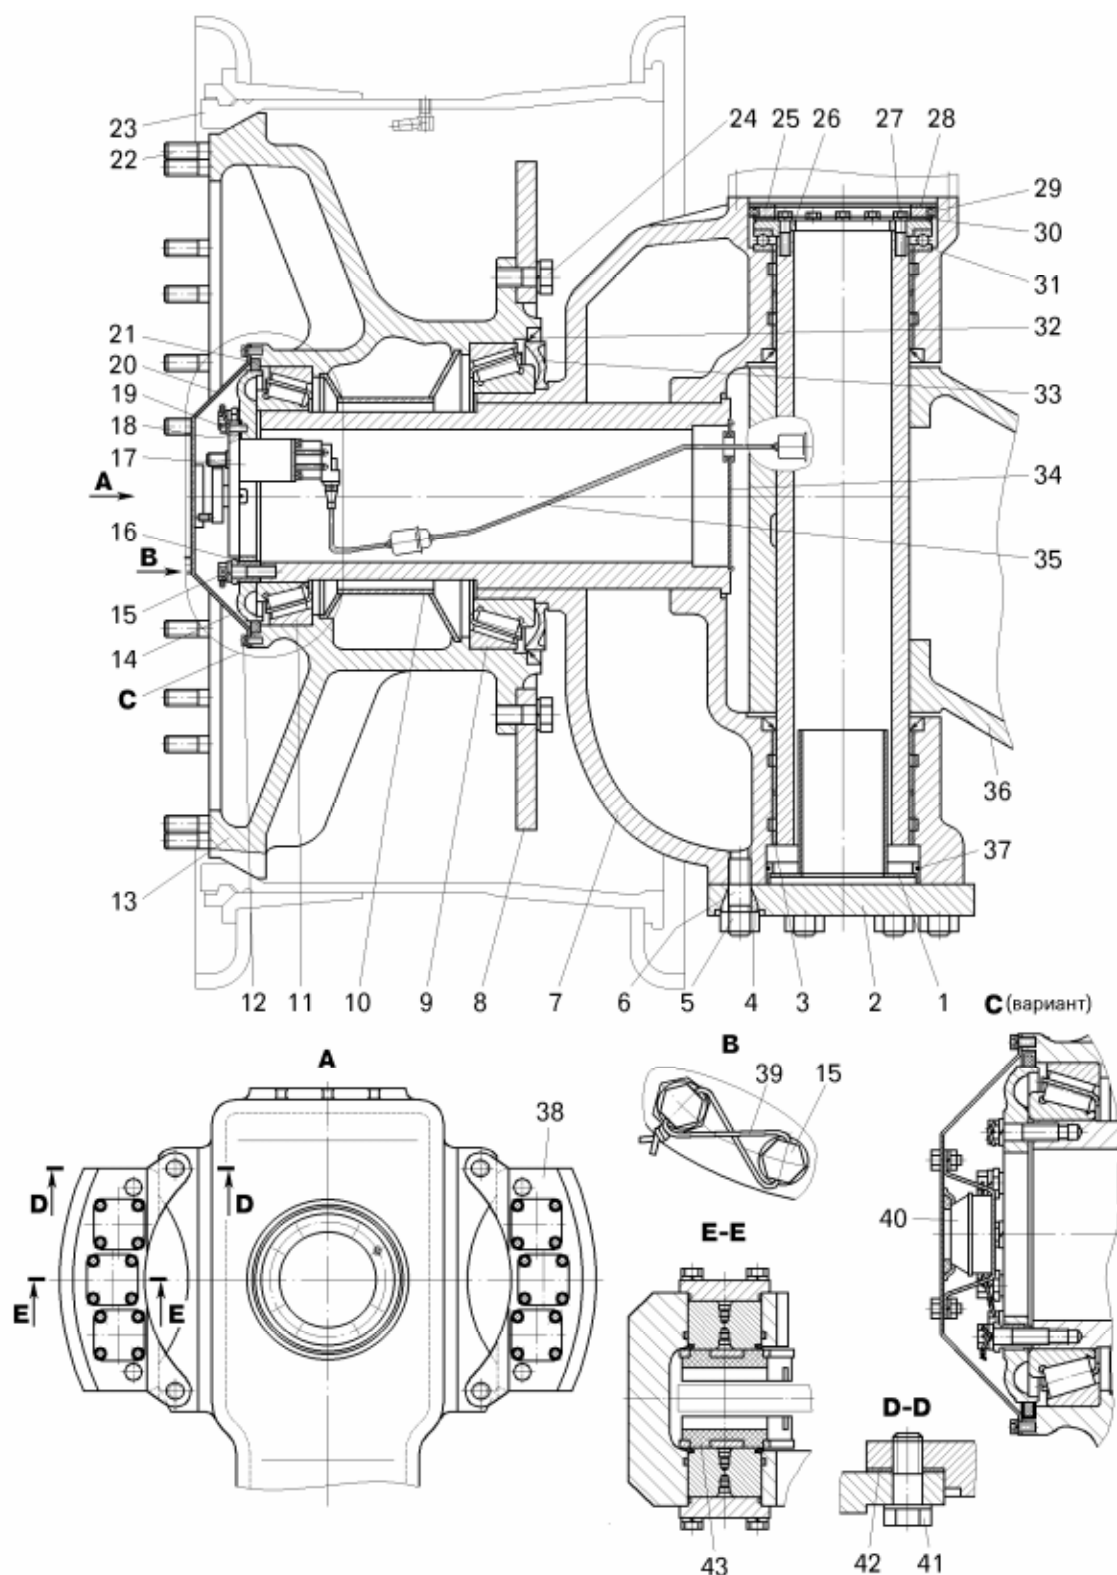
Кулак поворотный со ступицей, тормозом и механизмом поворота:
